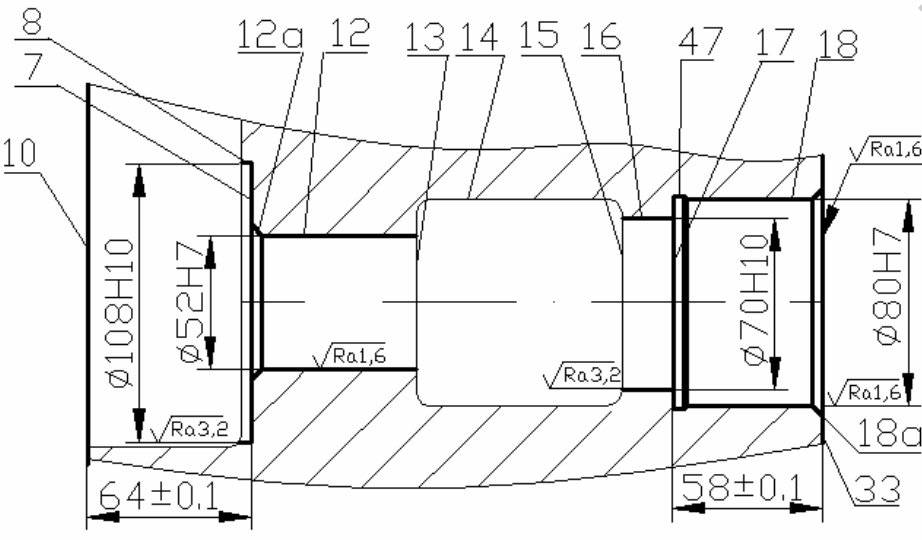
Эскиз детали с нумерацией поверхностей и обозначением осей
